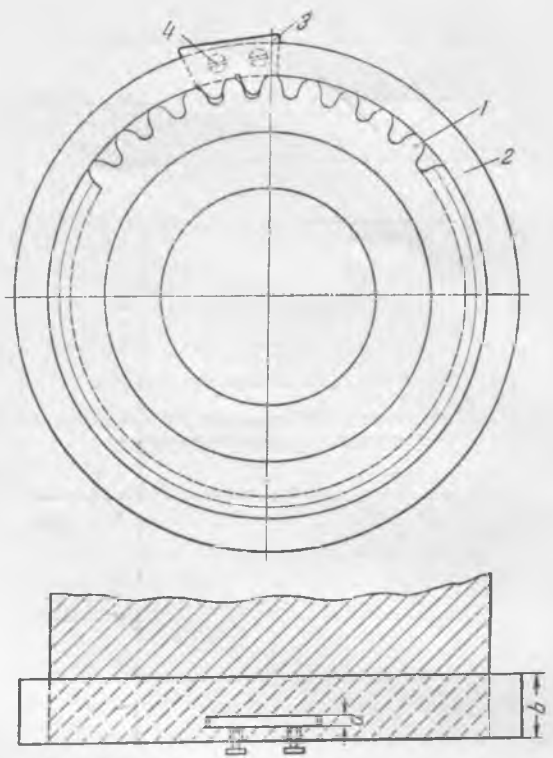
Исправления профиля зубьев шестерни по эвольвентному шаблону.
